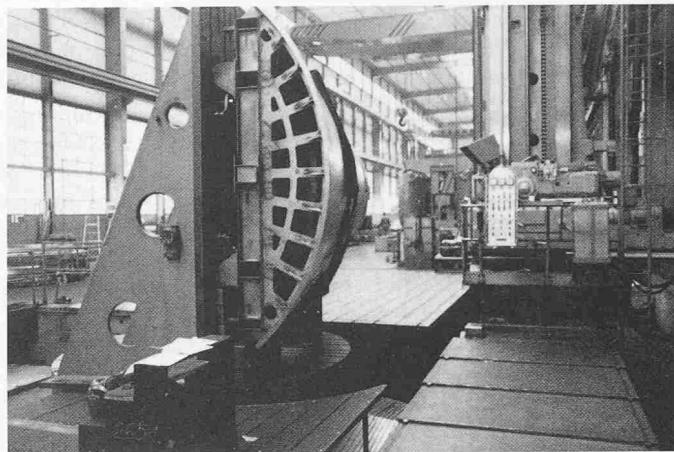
Dimensionskontrolle auf der Werkzeugmaschine
